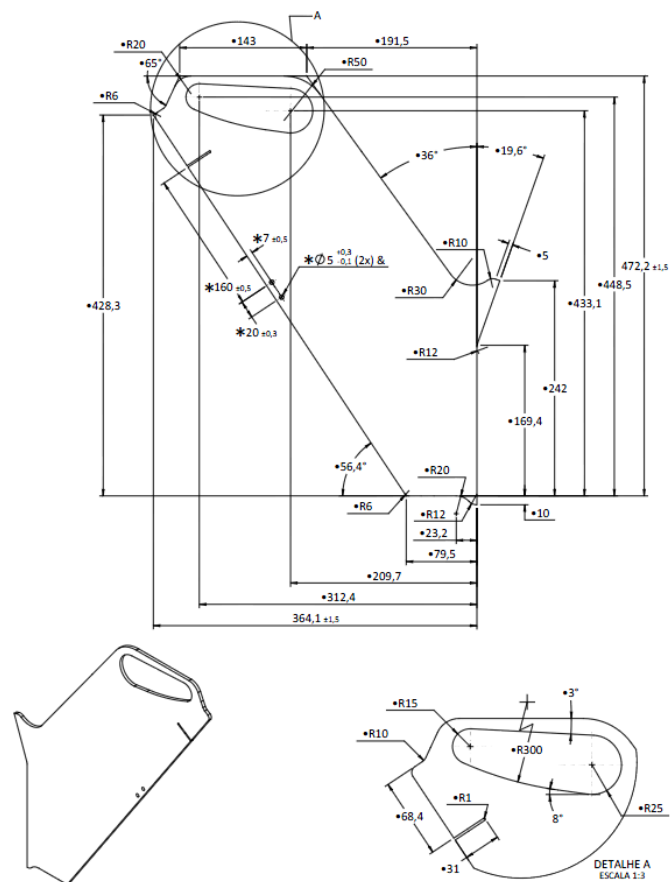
Detalhe dimensional do reforço de ligação da travessa e suporte frontal
